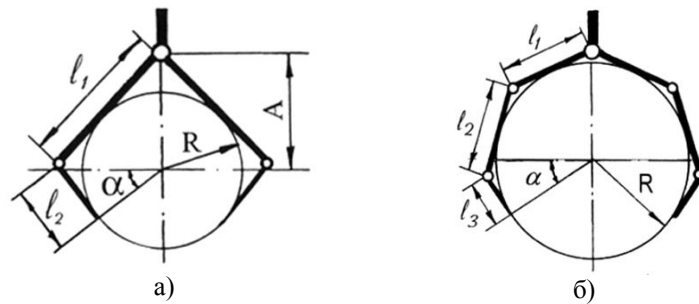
Особливості утримання циліндричних деталей двопальцевими захватними пристроями:
